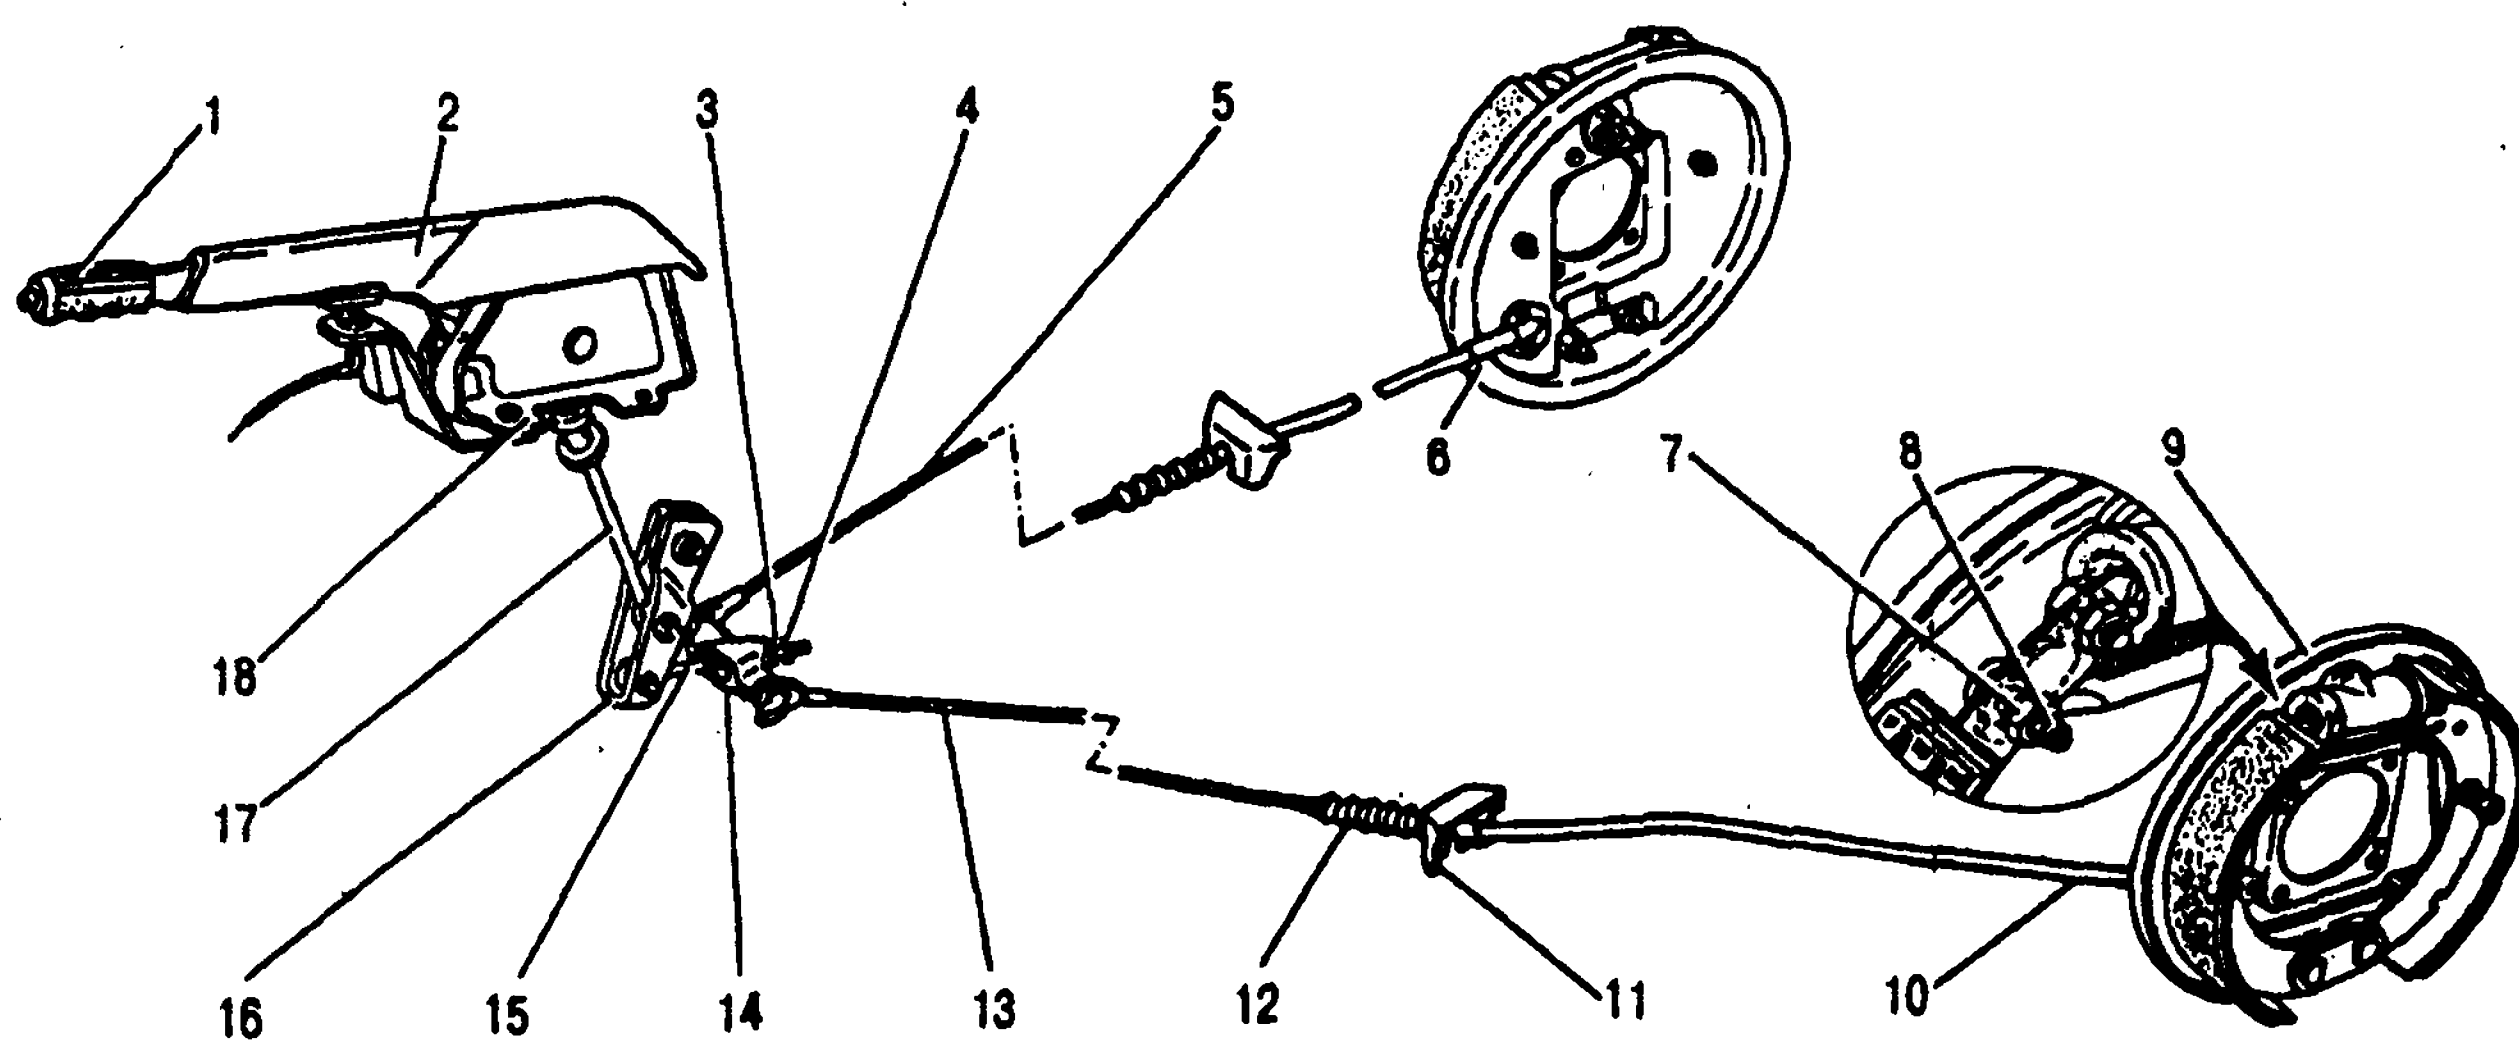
Стояночная тормозная система: 1 - ручка; 2 - декоративная облицовка; 3, 7 - гайки; 4 - контргайка; 5, 13 - троса; 6, 9 - задние тормозные механизмы; 8 - регулировочный эксцентрик; 10 - оболочка троса; 11 - упорный кронштейн; 12 - чехол; 14 - уравниватель; 15 - тяга уравнивателя; 16 - рычаг; 17 - тяга рычага; 18 - кронштейн
